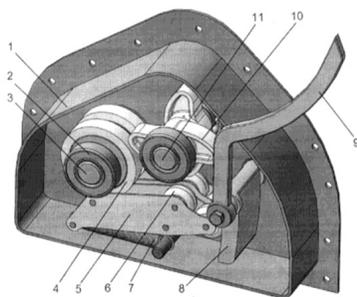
Внешний вид отечественного редуктора-вариатора
